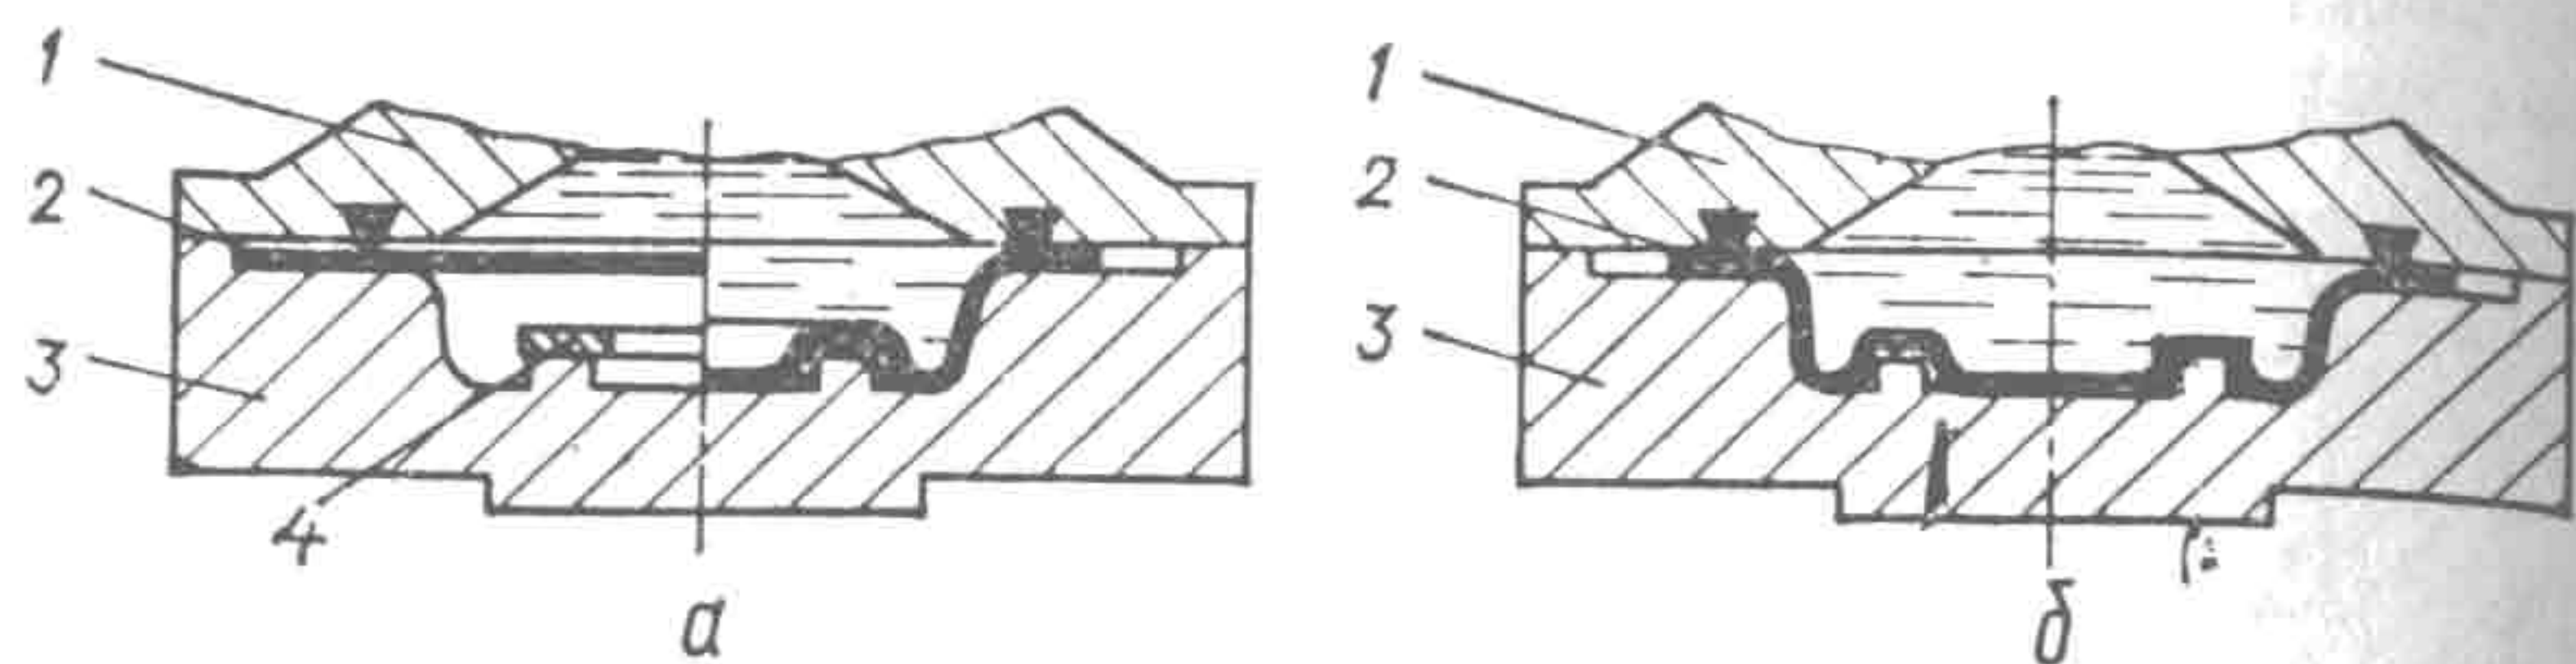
Схема калибровки радиусов с использованием резиновых накладок:
